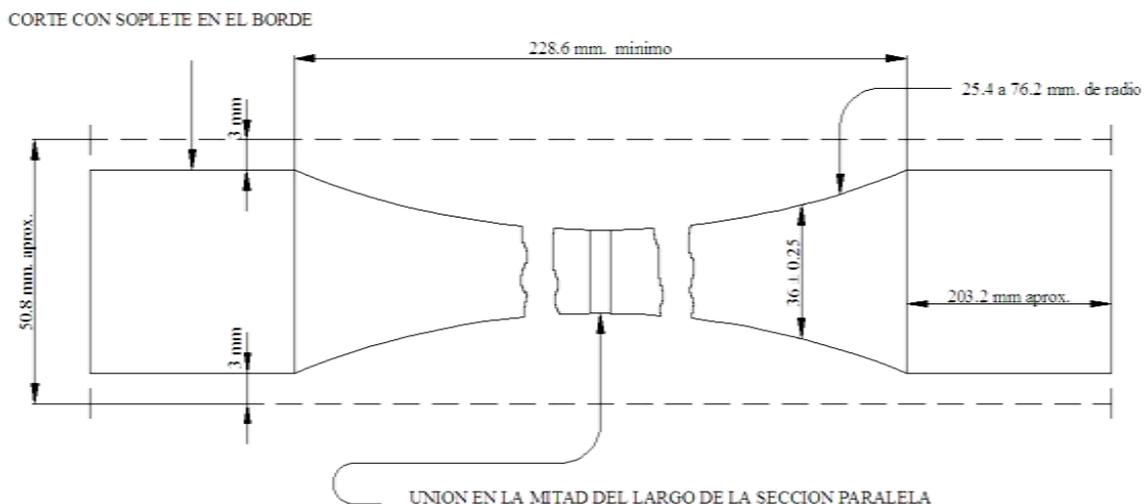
Probeta para prueba a tensión de soldadura [3]
